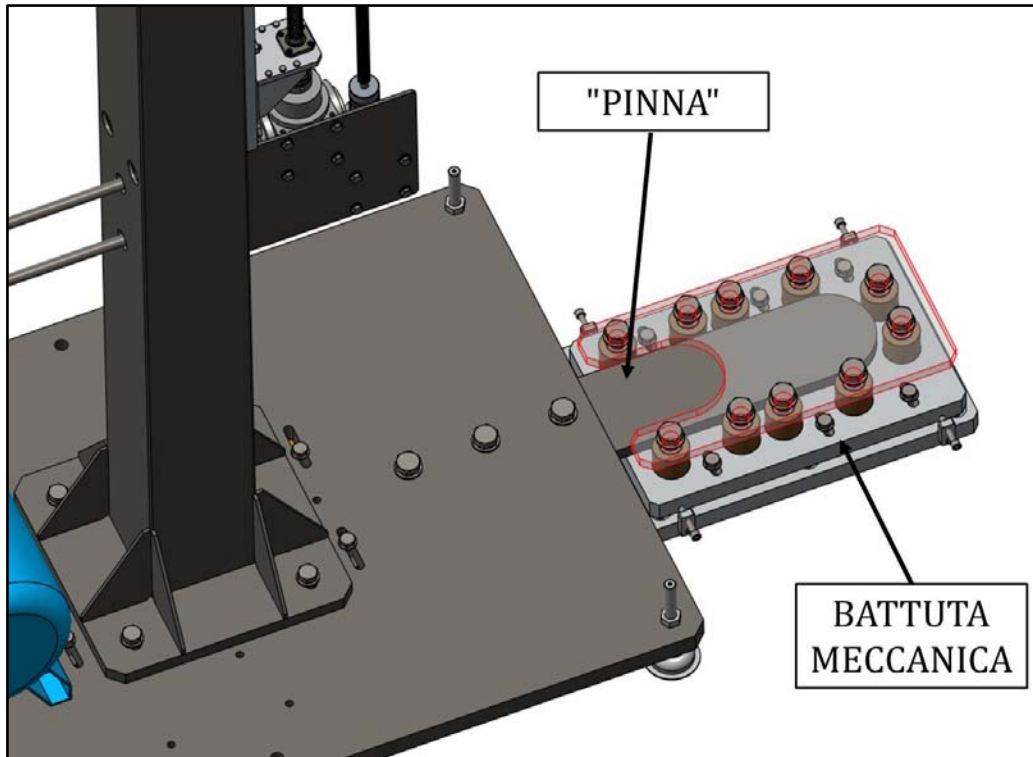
Centraggio della macchina di backup sulla battuta meccanica.
